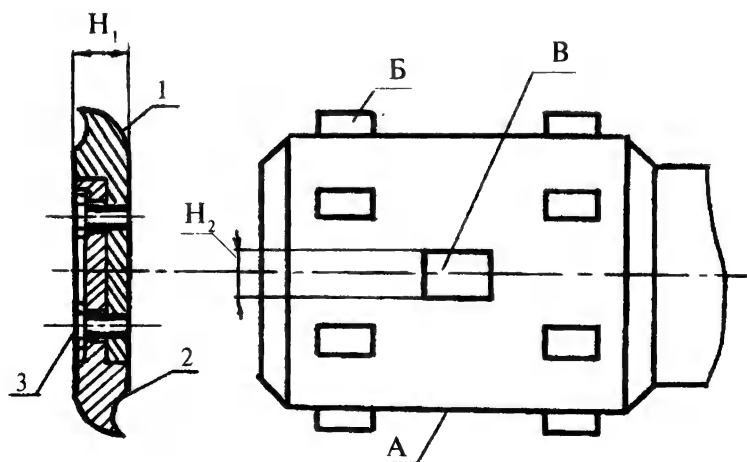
Расточная головка с плавающей пластиной (роймой): 1, 2 - резец, 3 - винт
